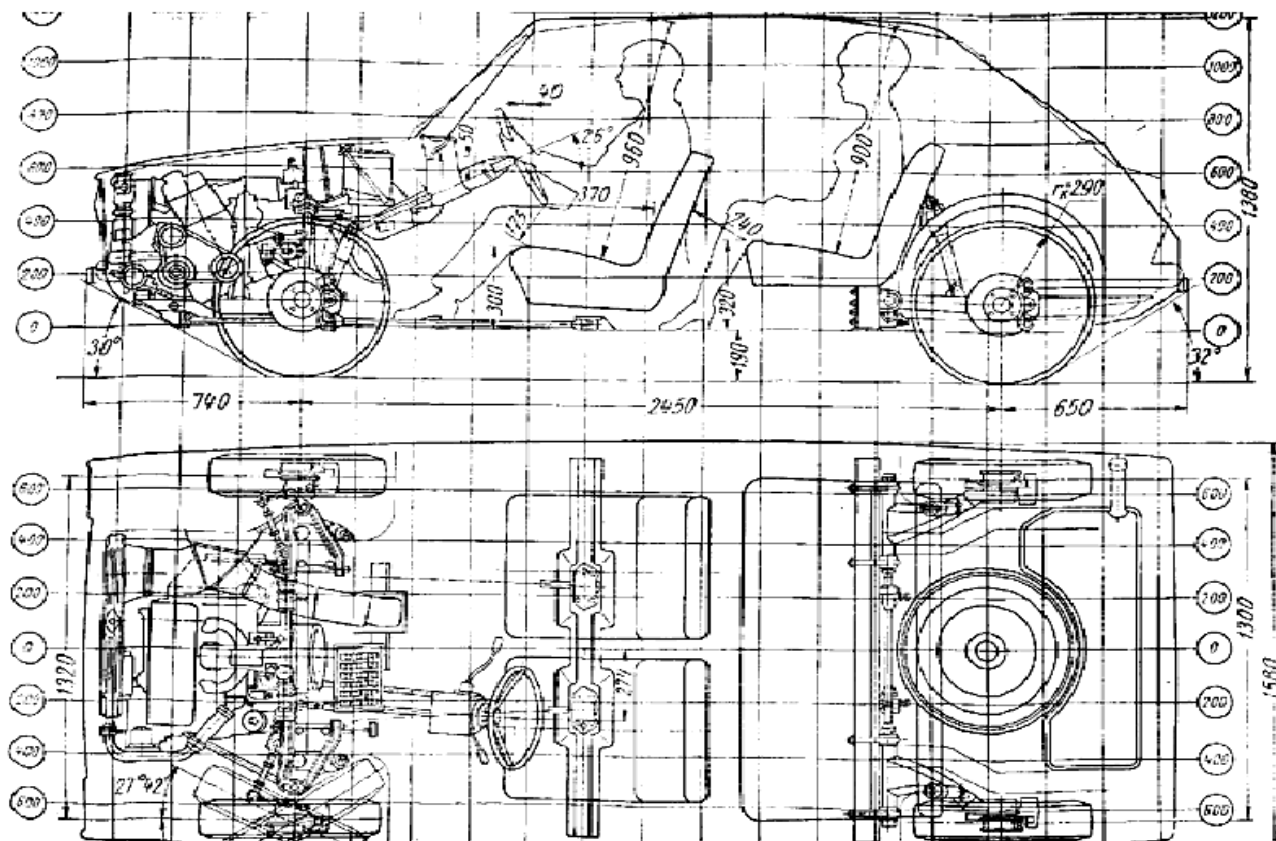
Чертеж общей компоновки легкового автомобиля
